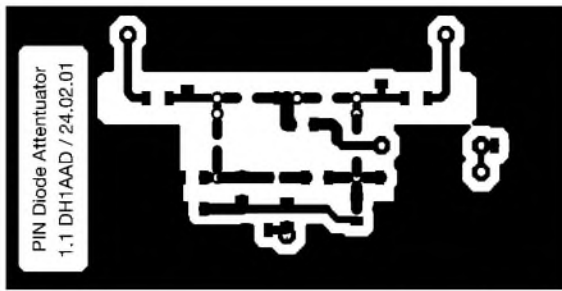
Das Layout des Abschwächers wurde für SMD-Bauteile entworfen, kann aber teilweise auch bedrahtete Bauelemente aufnehmen.
